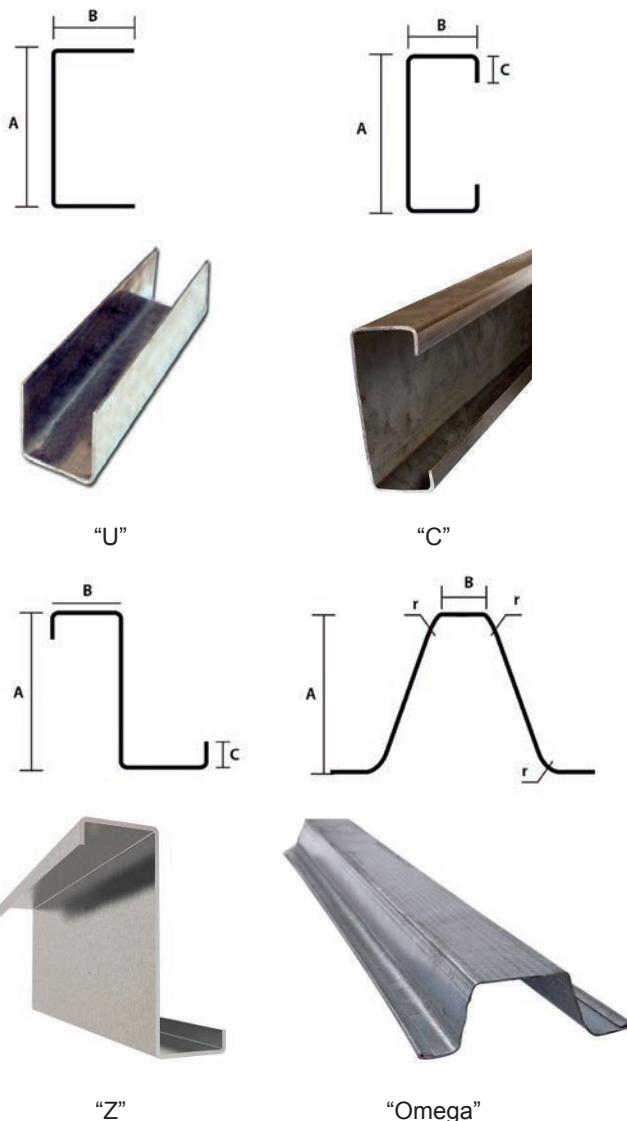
Tipos de perfiles de sección abierta conformados en frío y perfilados
